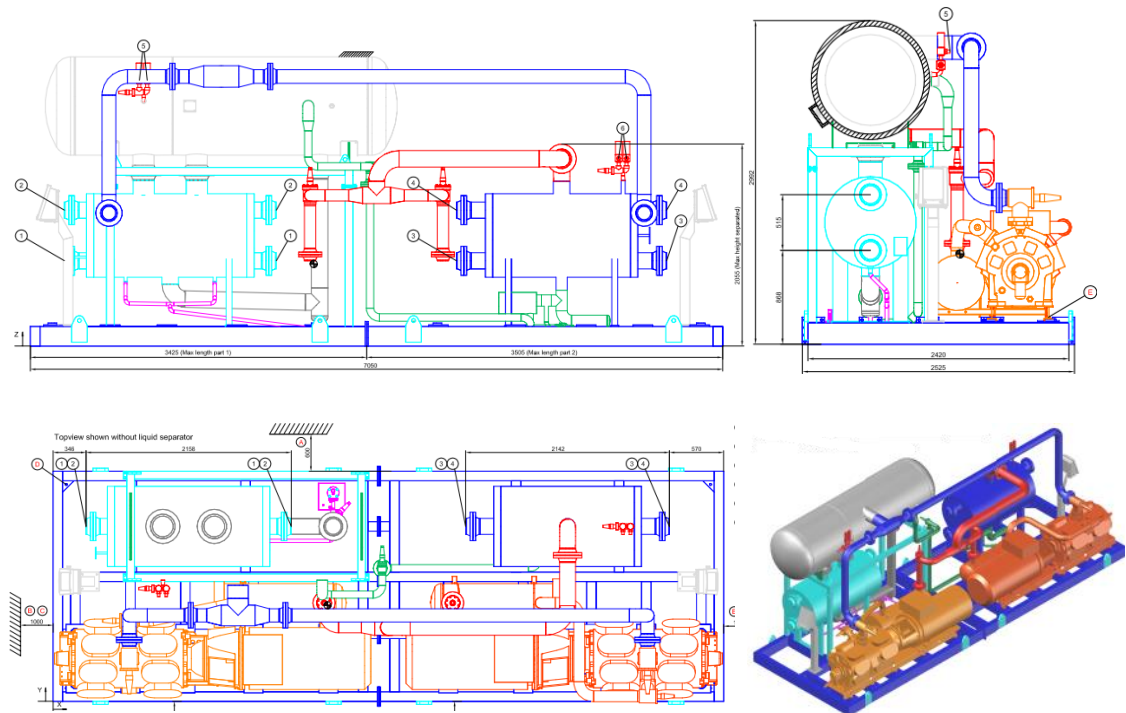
Kältemaschine mit Kolbenverdichter „Johnsons Controls“ – Technische Zeichnung
